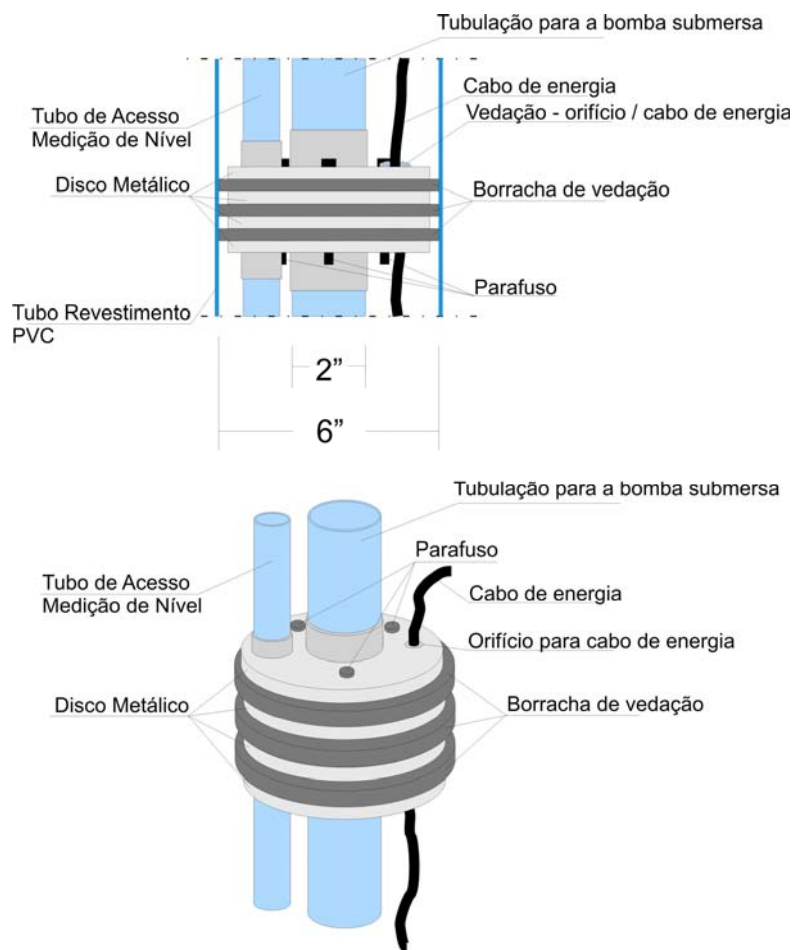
Esquema do detalhamento para a construção do packer.
